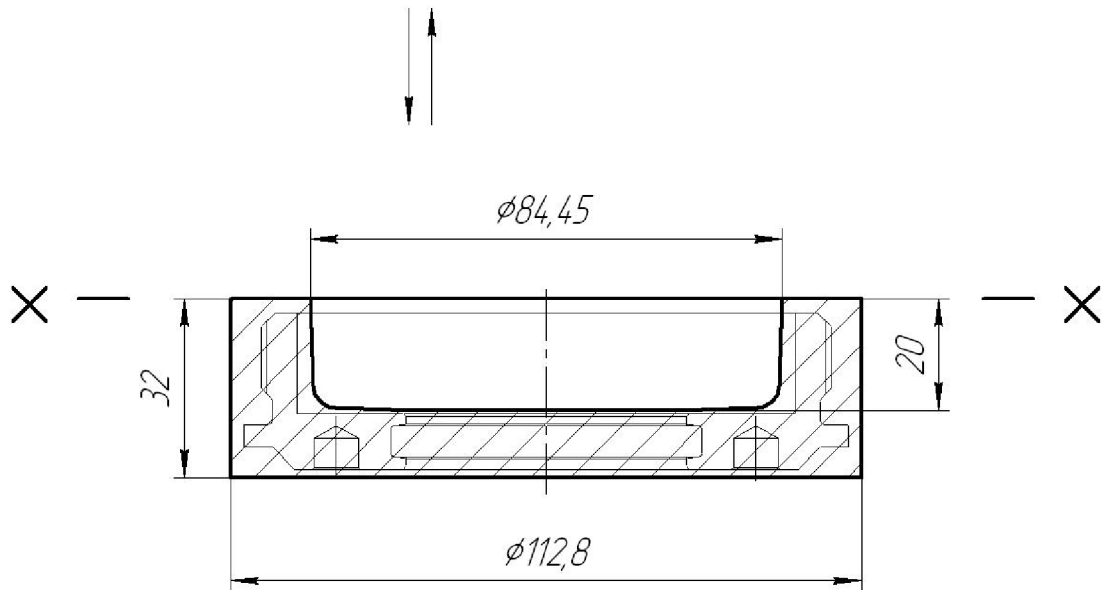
Ескіз заготовки, виготовленої на КГШП
